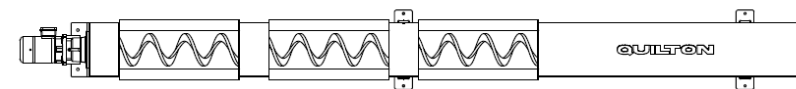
Vista en planta del cargol d'extracció (suports cada 3 metres)
